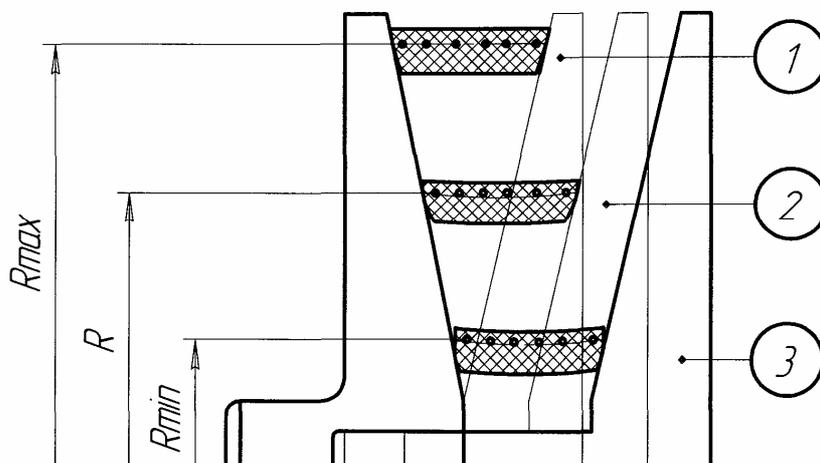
Контакт вариаторного ремня со шкивом при регулировании передаточного числа вариатора.
